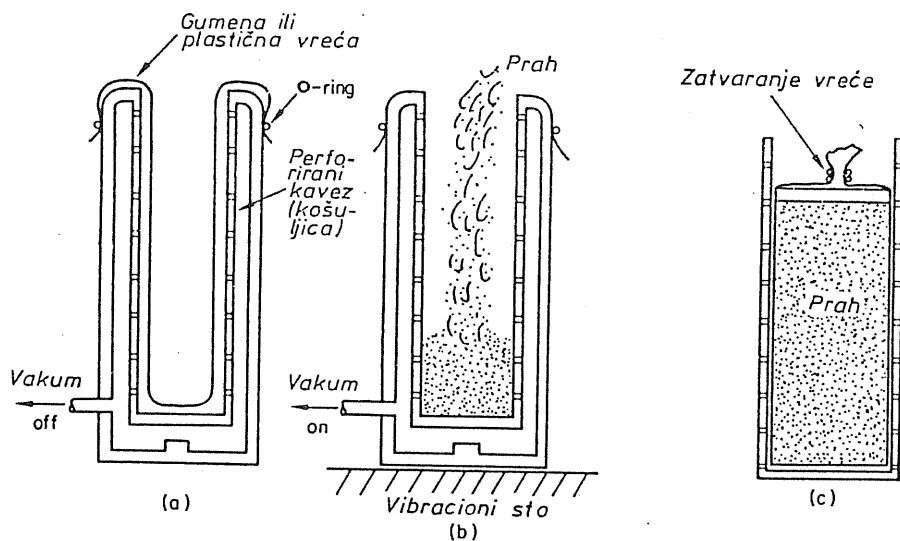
Blok šema postrojenja za izostatičko sabijanje praha /20/
